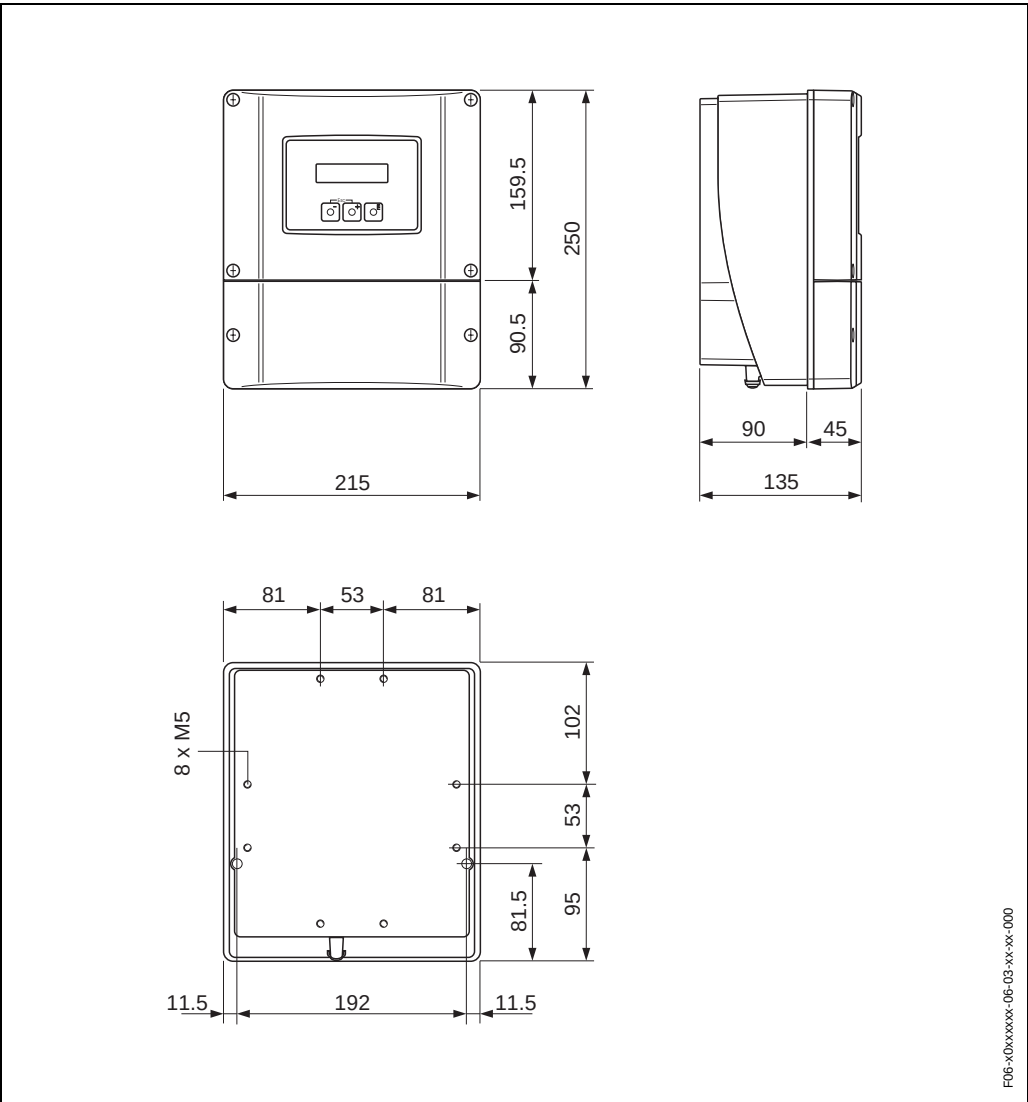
Dimensoes do alojamento de montagem de parede(para instalacao em painel e montagem de tubo → Pag. 44)
